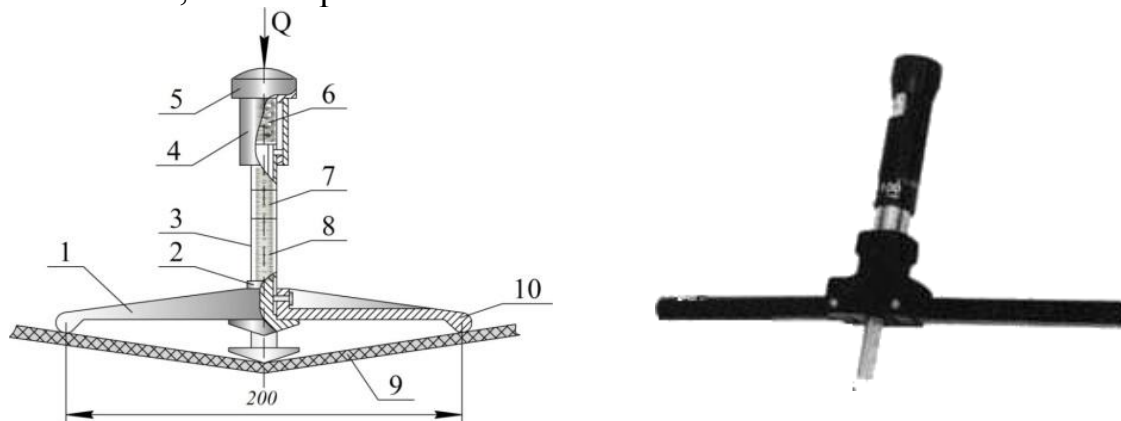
Приспособление для контроля натяжения ремней: 1 – планка; 2 – установочное кольцо; 3 – стержень; 4 – насадка; 5 – колпачок; 6 – пружина; 7, 8 – шкалы; 9 – ремень; 10 – бортики
